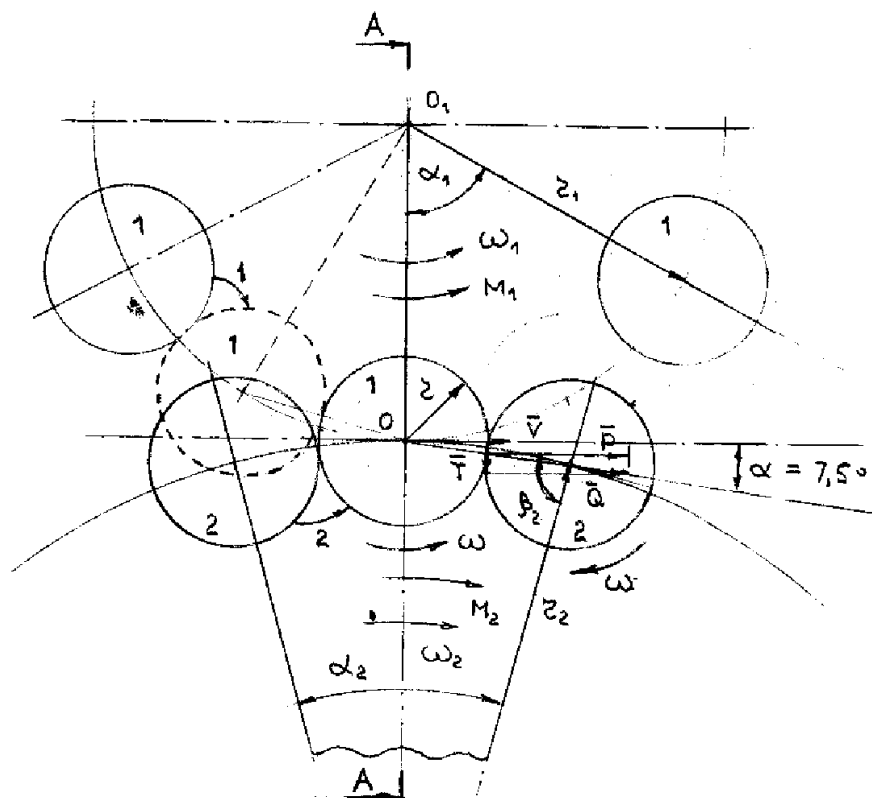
Передача с относительно подвижными цилиндрическими поверхностями зацепления (в зацеплении один элемент первого колеса)
